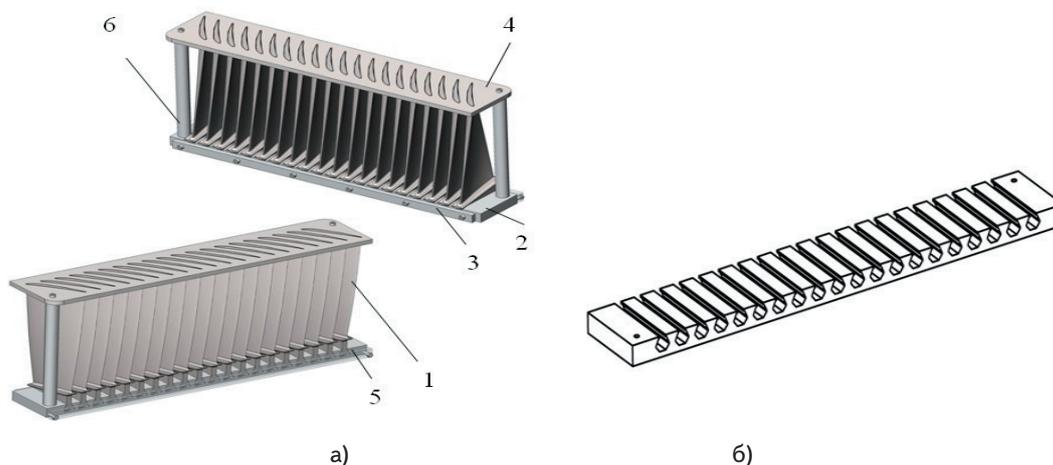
Многоместное приспособление для установки лопаток: а – общий вид приспособления; б – кассета для установки лопаток
